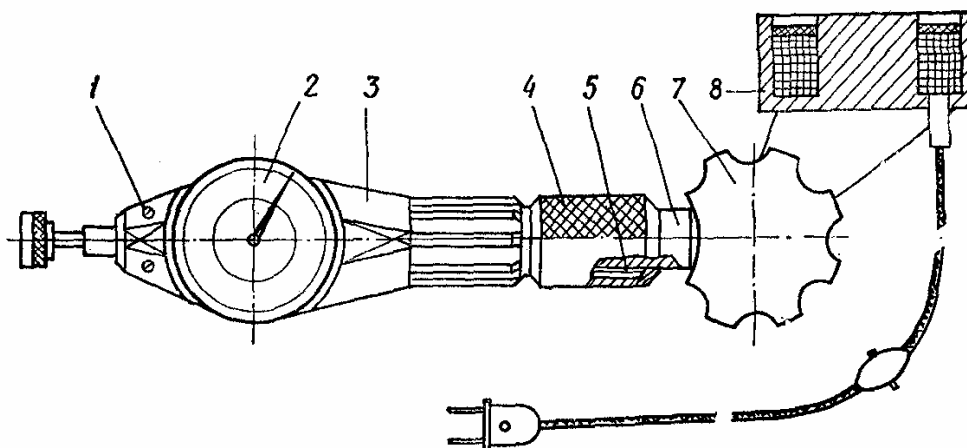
Пристосування КИ-4902 для перевірки карданних валів:
